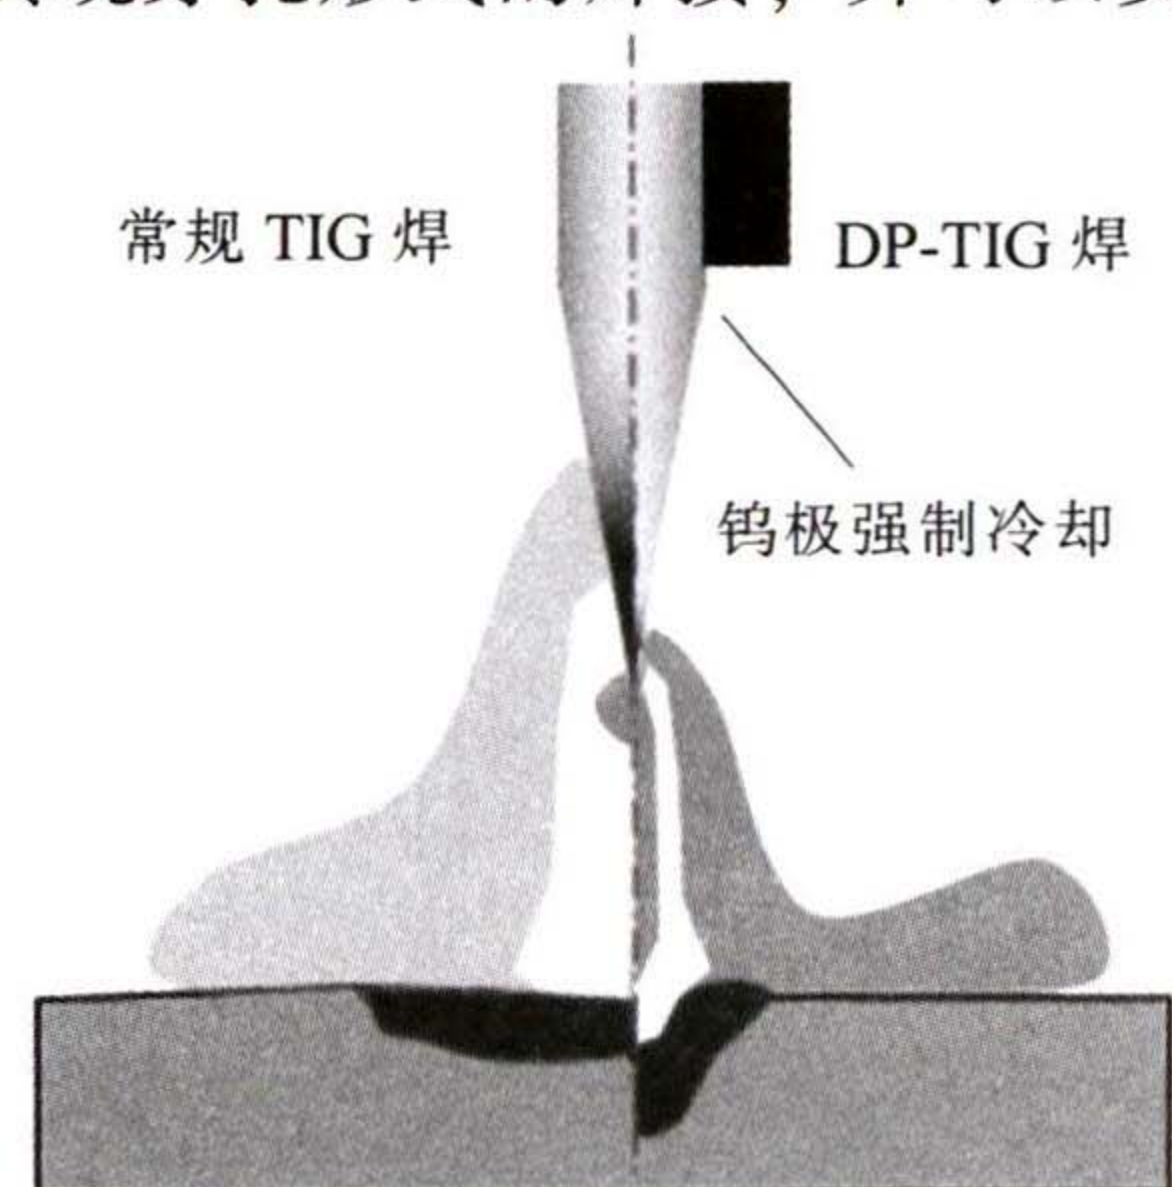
常规 TIG 焊与 DP-TIG 焊原理对比
